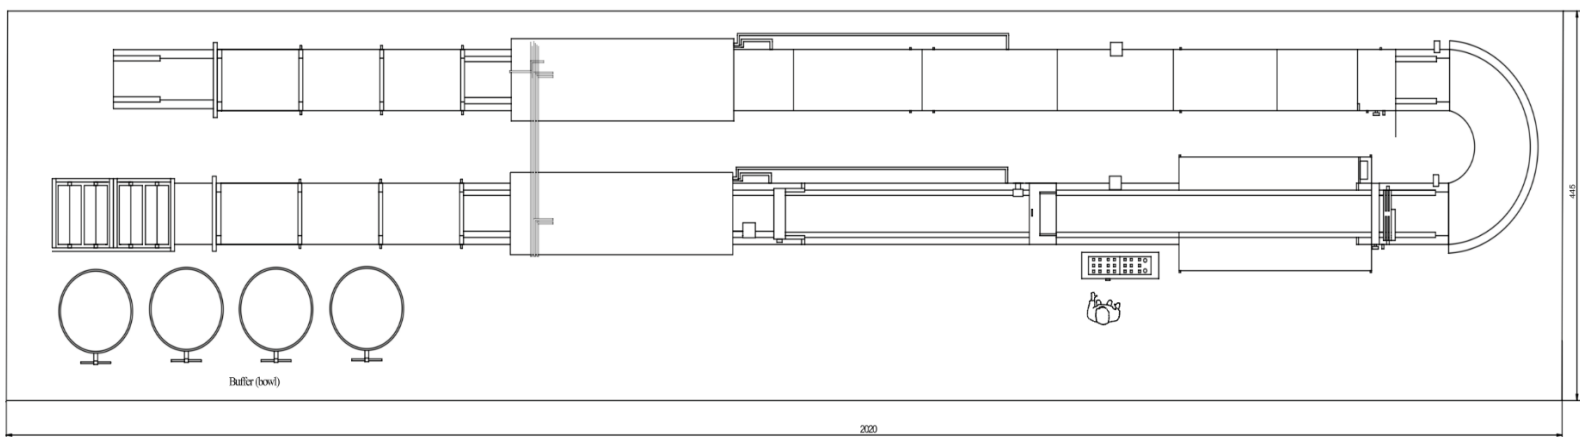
Vista superior área de moldeado y corte para snacks bar (medidas en cm)
